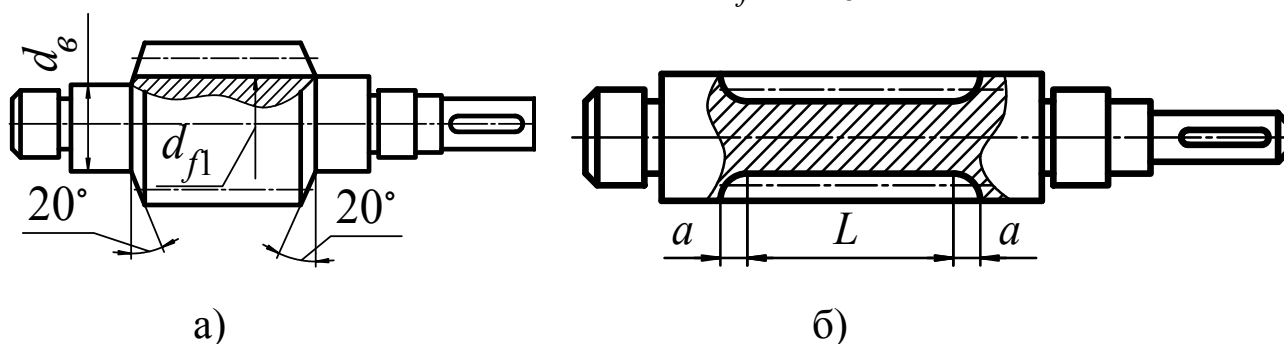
Конструктивні варіанти виконання черв'яків
